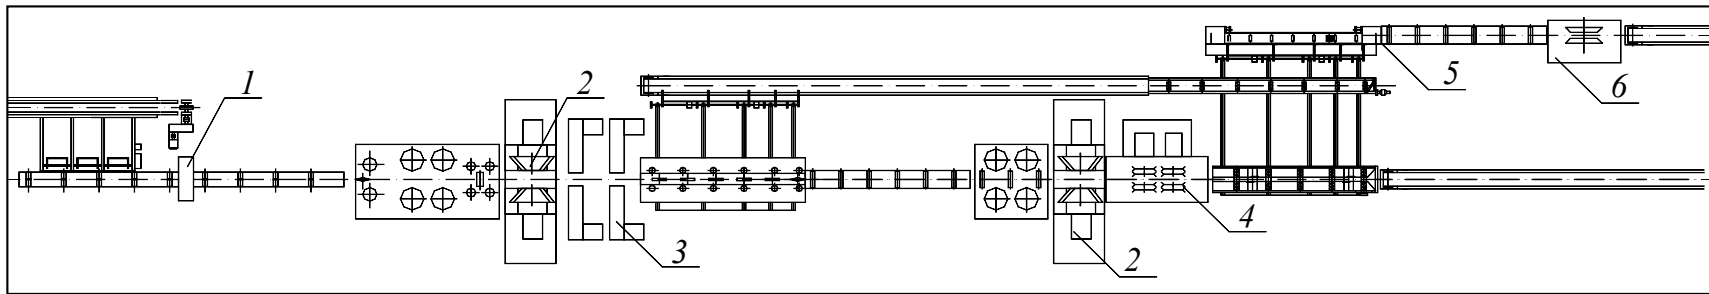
Схема расположения оборудования в цехе на базе ленточнопильных и круглопильных станков с фрезерными приставками:
